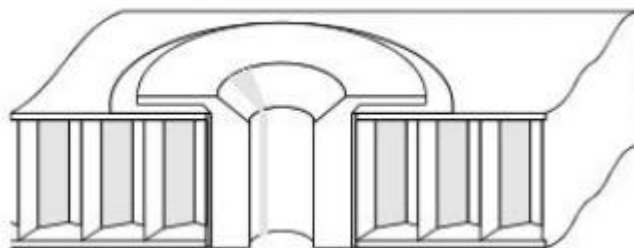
Vlepená hrana vhodná pro silnější panely [12]
